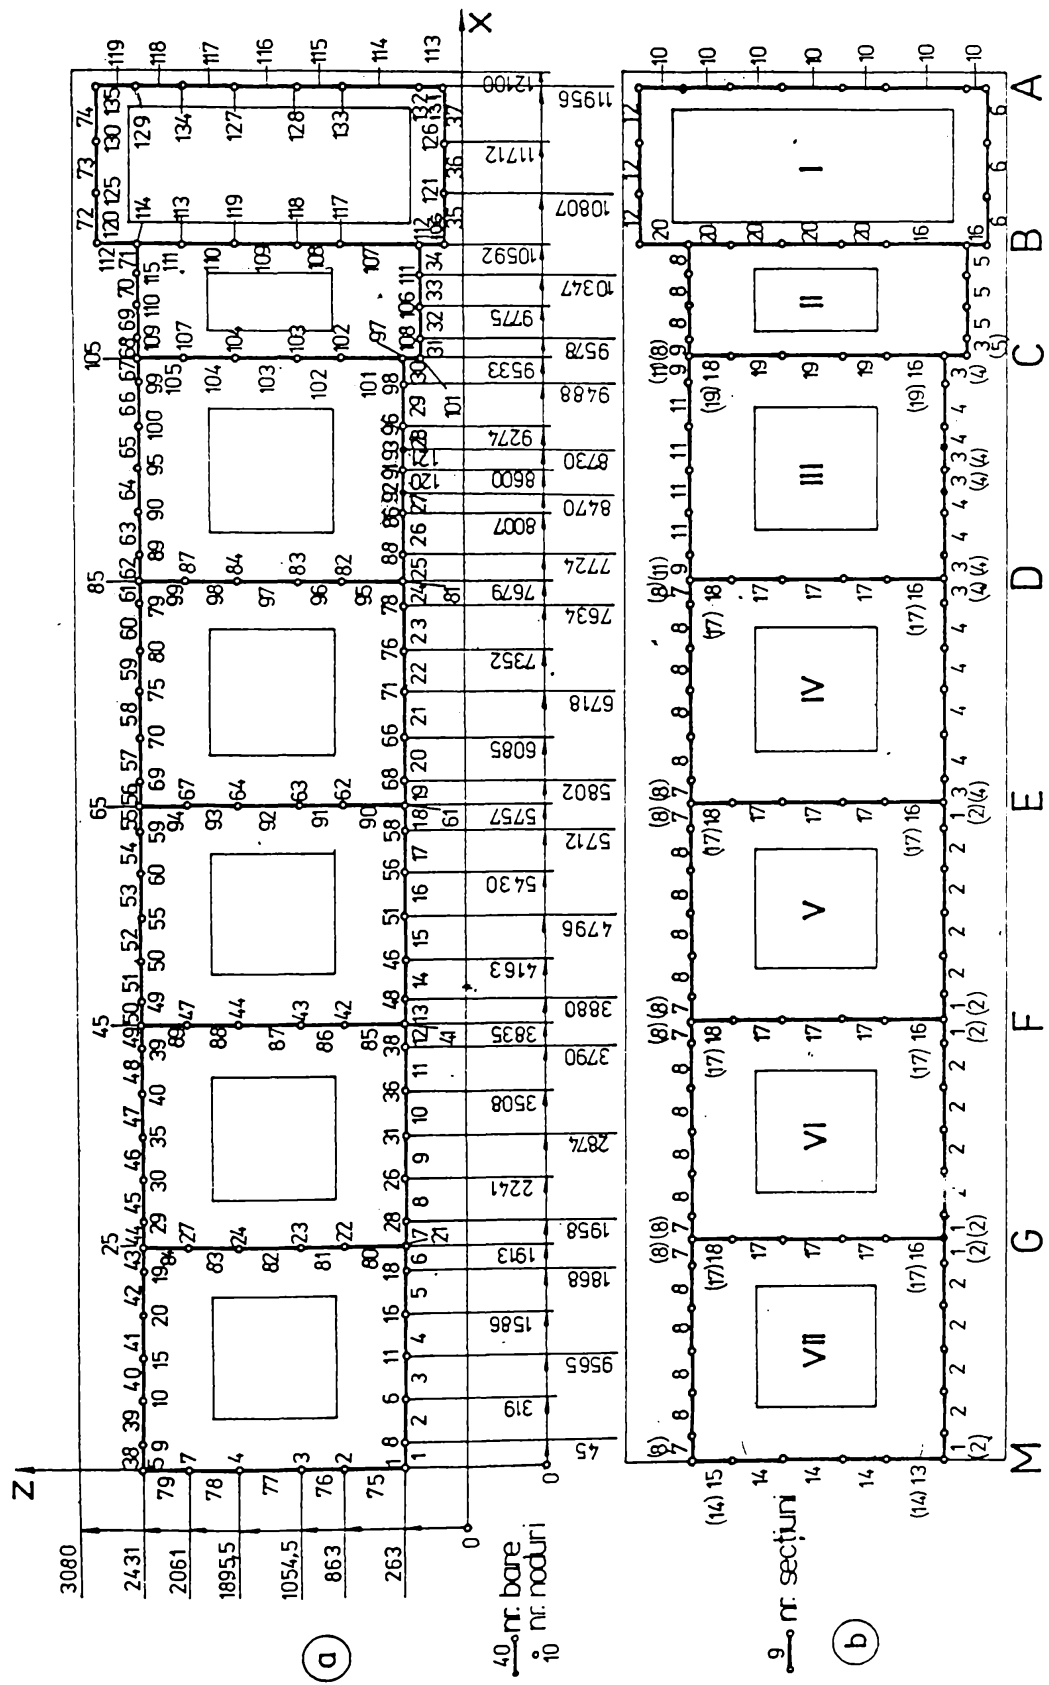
STRUCTURA PLANĂ A VAGONULUI ALCĂTUITĂ DIN ELEMENTE FINITE DE TIP GRINDĂ - VARIANTA V.P.G.1. și V.P.G.2.
